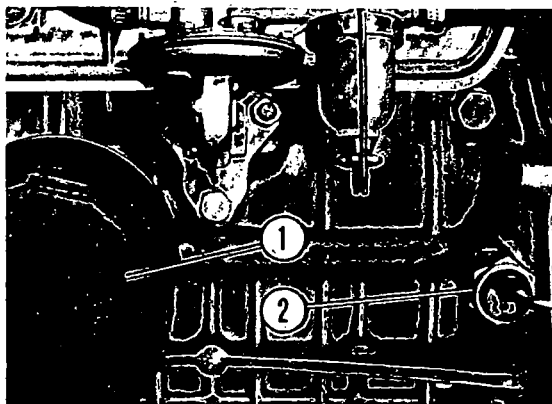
Vypouštěcí šroub ve spodním víku motoru
